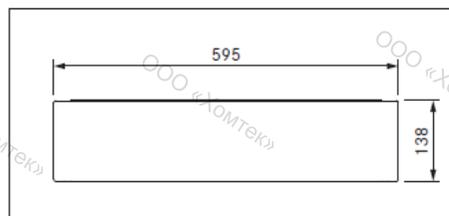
Размеры прибора, модель MSS140, вид спереди
